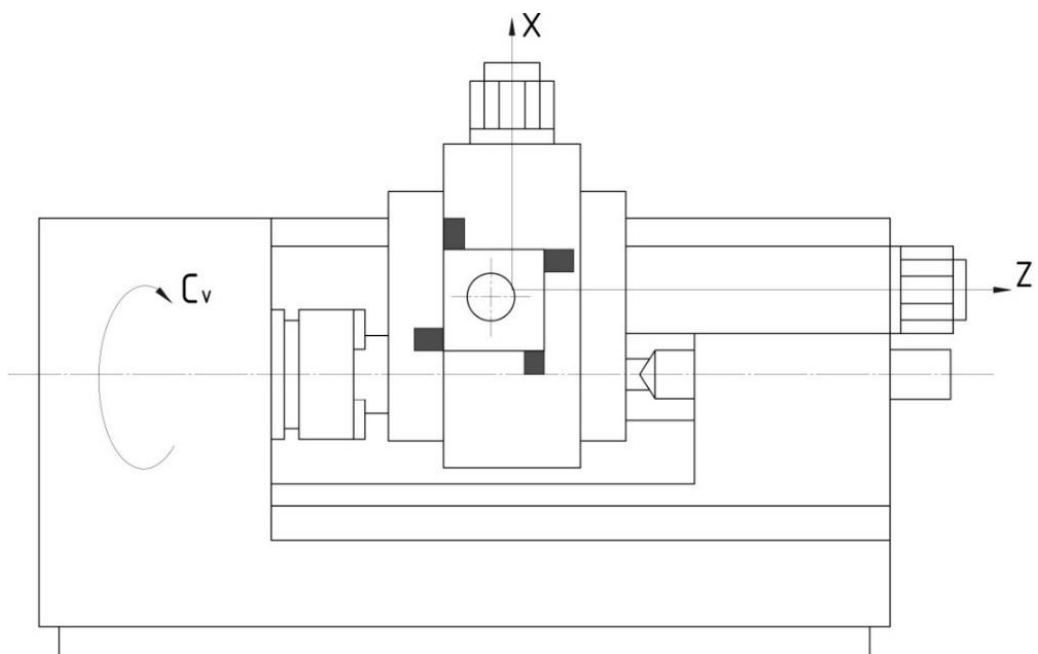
Компоновка токарного верстата (Варіант 2)
